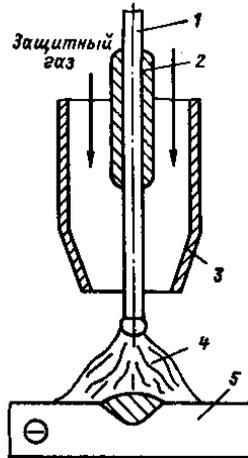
Схема процесса сварки в среде защитных газов плавящимся электродом:
